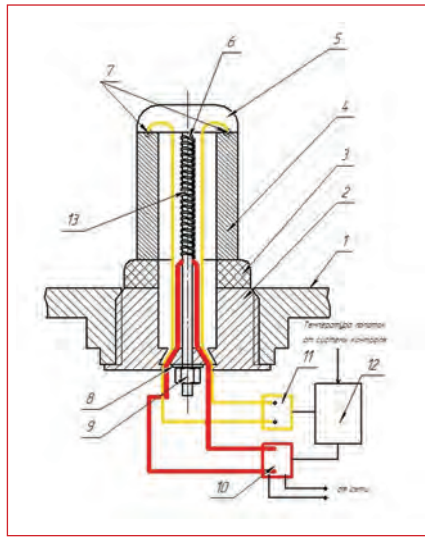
Устройство для контроля в эксплуатации деградации материала и защитных покрытий турбинных лопаток газотурбинных двигателей («Свидетель»): 1 – корпус газотурбинного двигателя; 2 – корпус устройства; 3 – тепловой изолятор; 4 – образец; 5 – крышка; 6 – электронагреватель; 7 – термопары; 8 – шайба; 9 – гайка; 10 – регулятор силы тока; 11 – устройство усиления сигналов термопар; 12 – устройство контроля и управления; 13 – стержень
